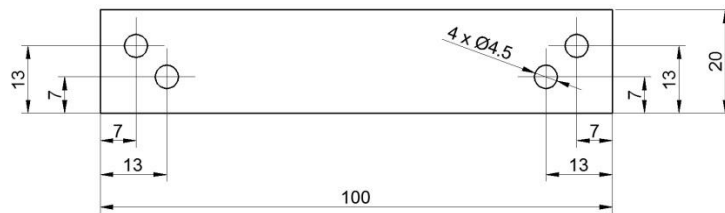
Widok spodniej strony konstrukcji szkieletowej ramki tylnej
